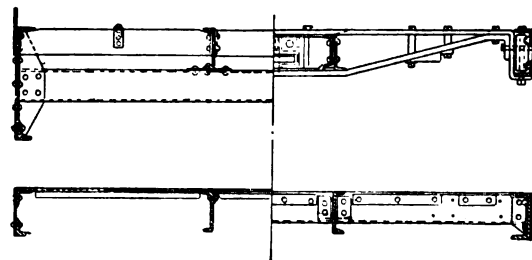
, 3, 4 e 5. — Sezioni diverse del telaio delle vetture in acciaio della Boston Elevated Railway Company.
